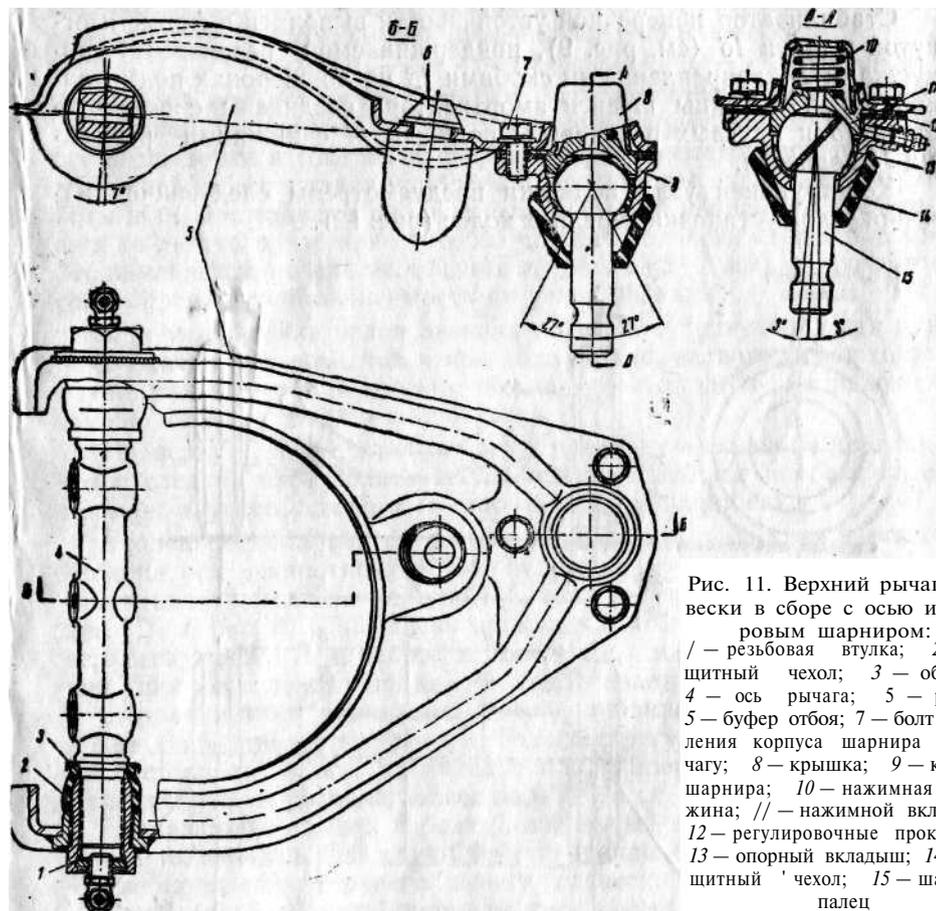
Верхний рычаг подвески в сборе с осью и шаровым шарниром: 1 — резьбовая втулка; 2 — защитный чехол; 3 — обойма; 4 — ось рычага; 5 — рычаг; 6 — буфер отбоя; 7 — болт крепления корпуса шарнира к рычагу; 8 — крышка; 9 — корпус шарнира; 10 — нажимная пружина; // — нажимной вкладыш; 12 — регулировочные прокладки; 13 — опорный вкладыш; 14 — защитный чехол; 15 — шаровой палец
